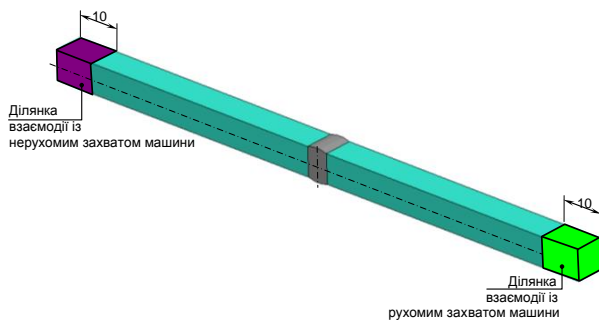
Розрахункова схема конструктивної системи зразка зварного з'єднання для випробувань
